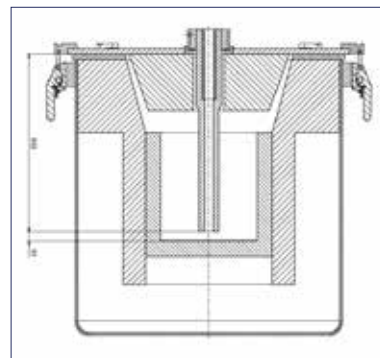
Schmelzofen Seitenansicht mit Steigrohrsystem
